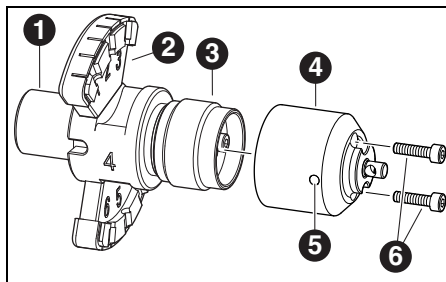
Componenti supporto del pezzo in lavorazione fresaggio rotante Ceramill
